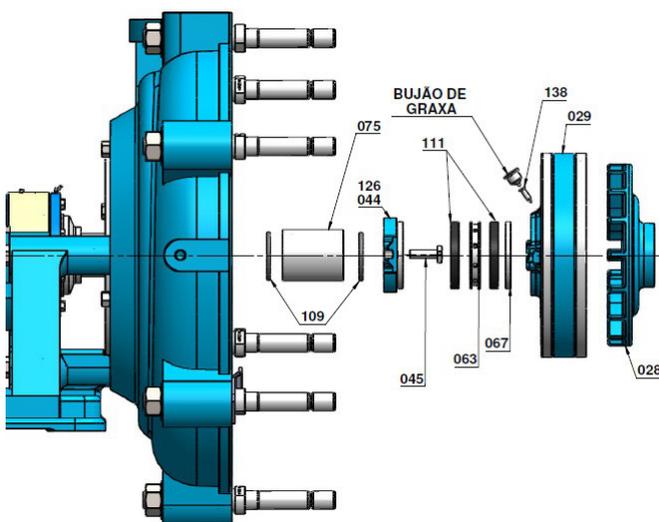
MONTAGEM - VEDAÇÃO CENTRÍFUGA METÁLICA
